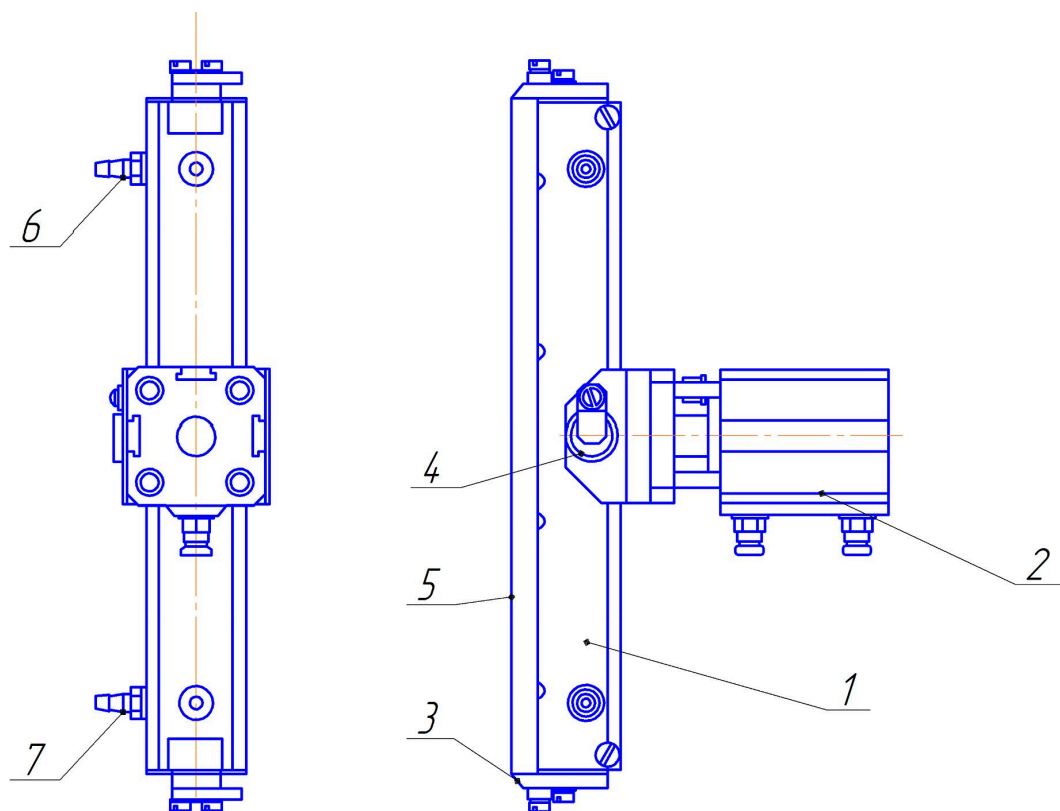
Механізм поздовжнього зварювання плівки:
